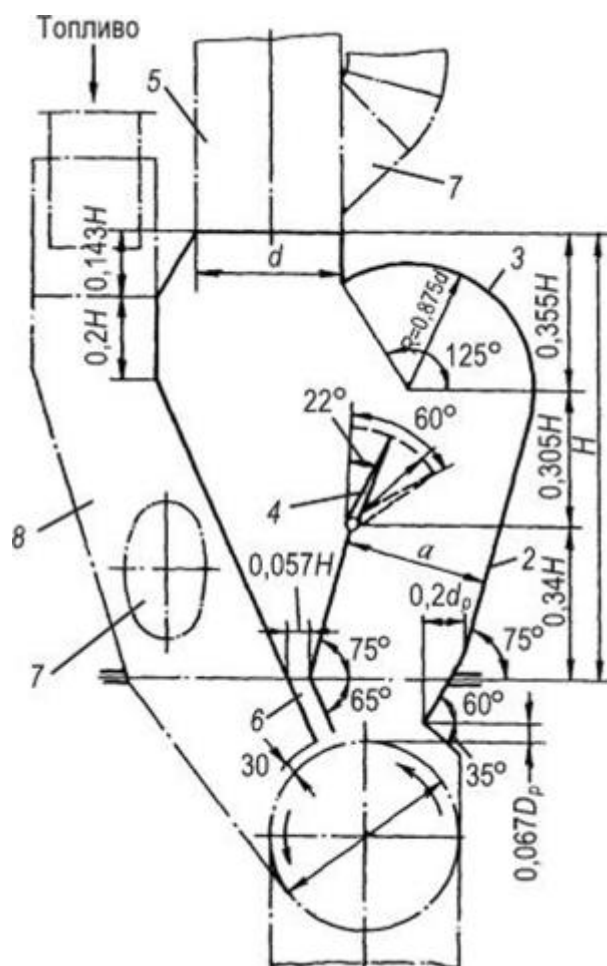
Інерційний сепаратор ВТ І [15]: 1 - вхідна частина сепаратора; 2 - корпус сепаратора; 3 - криволінійна верхня ділянка сепаратора; 4 - регулюючий шибер; 5- вихідний патрубок; 6 - тічка повернення; 7 - вибуховий клапан; 8 -течка основного палива
